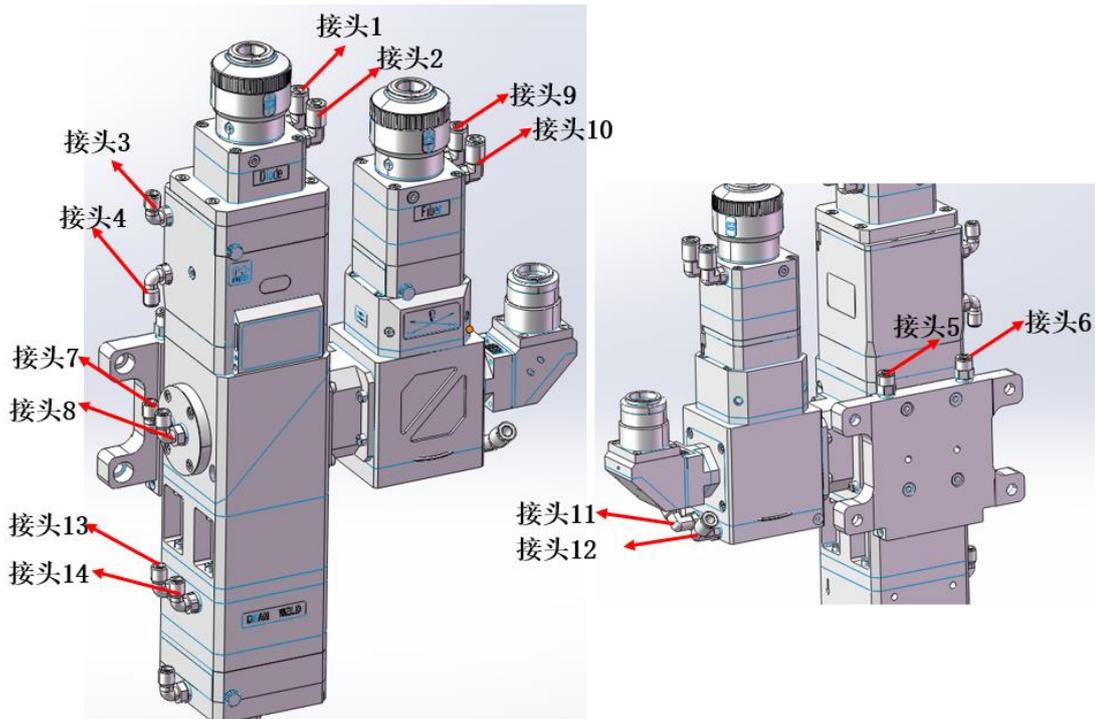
BW290 双波段焊接头安装尺寸图
